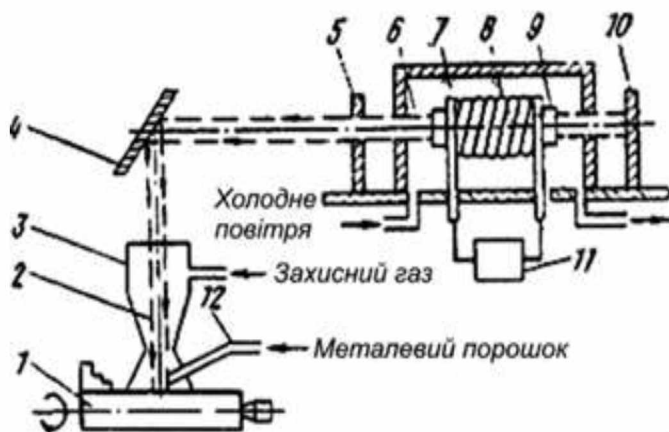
Схема установки для лазерного наплавлення [9].
